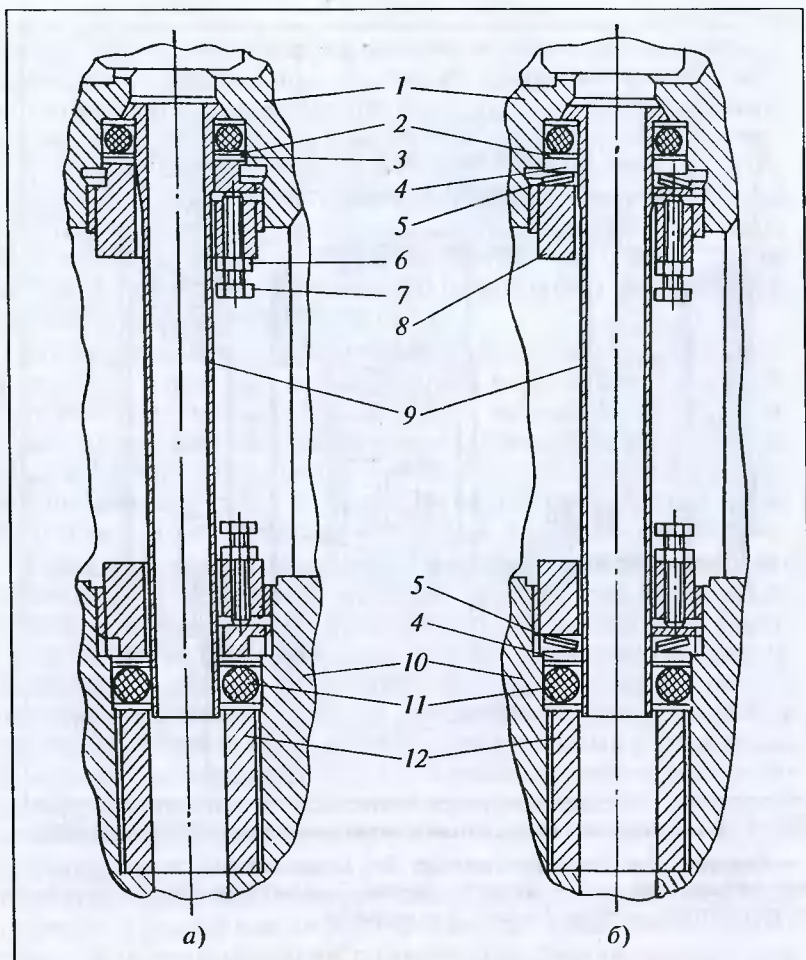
Радиальный узел водоподвода ротора электродвигателя типа АВ-8000/6000УЗ:
